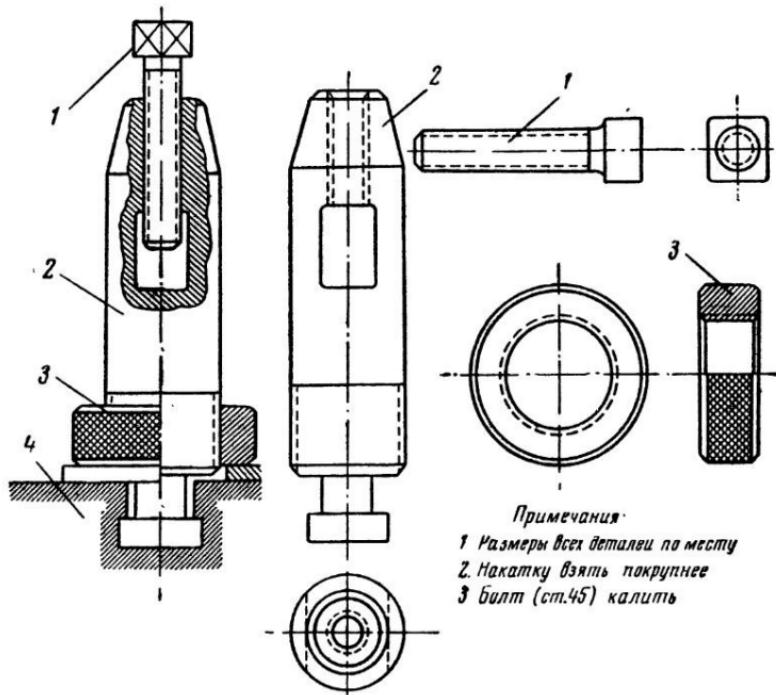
Дополнительный резцодержатель-«солдатик» для токарного станка, его детали и крепление к суппорту: 1 — болт крепления резца; 2 — корпус; 3 — гайка крепления резцодержателя; 4 — суппорт.
